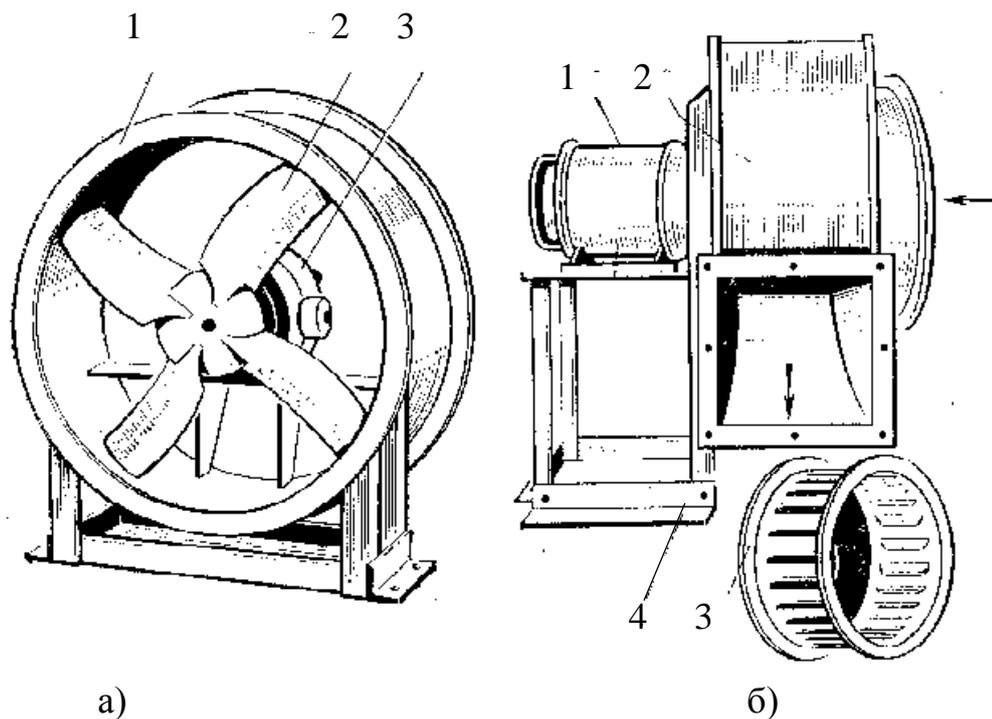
Вентиляторы: а) осевой: 1 – корпус; 2 – крыльчатка; 3 – электродвигатель; б) центробежный: 1 – электродвигатель; 2 – кожух; 3 – крыльчатка; 4 – станина
